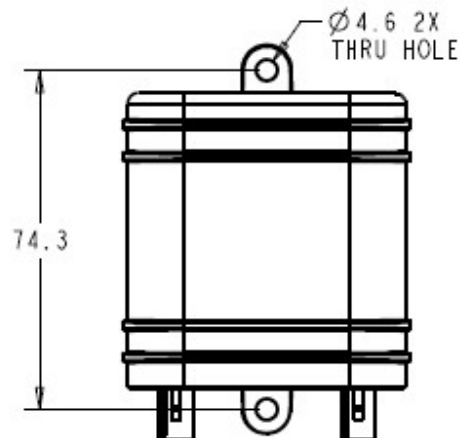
Dimensões de montagem do SkyPatrol TT8750
